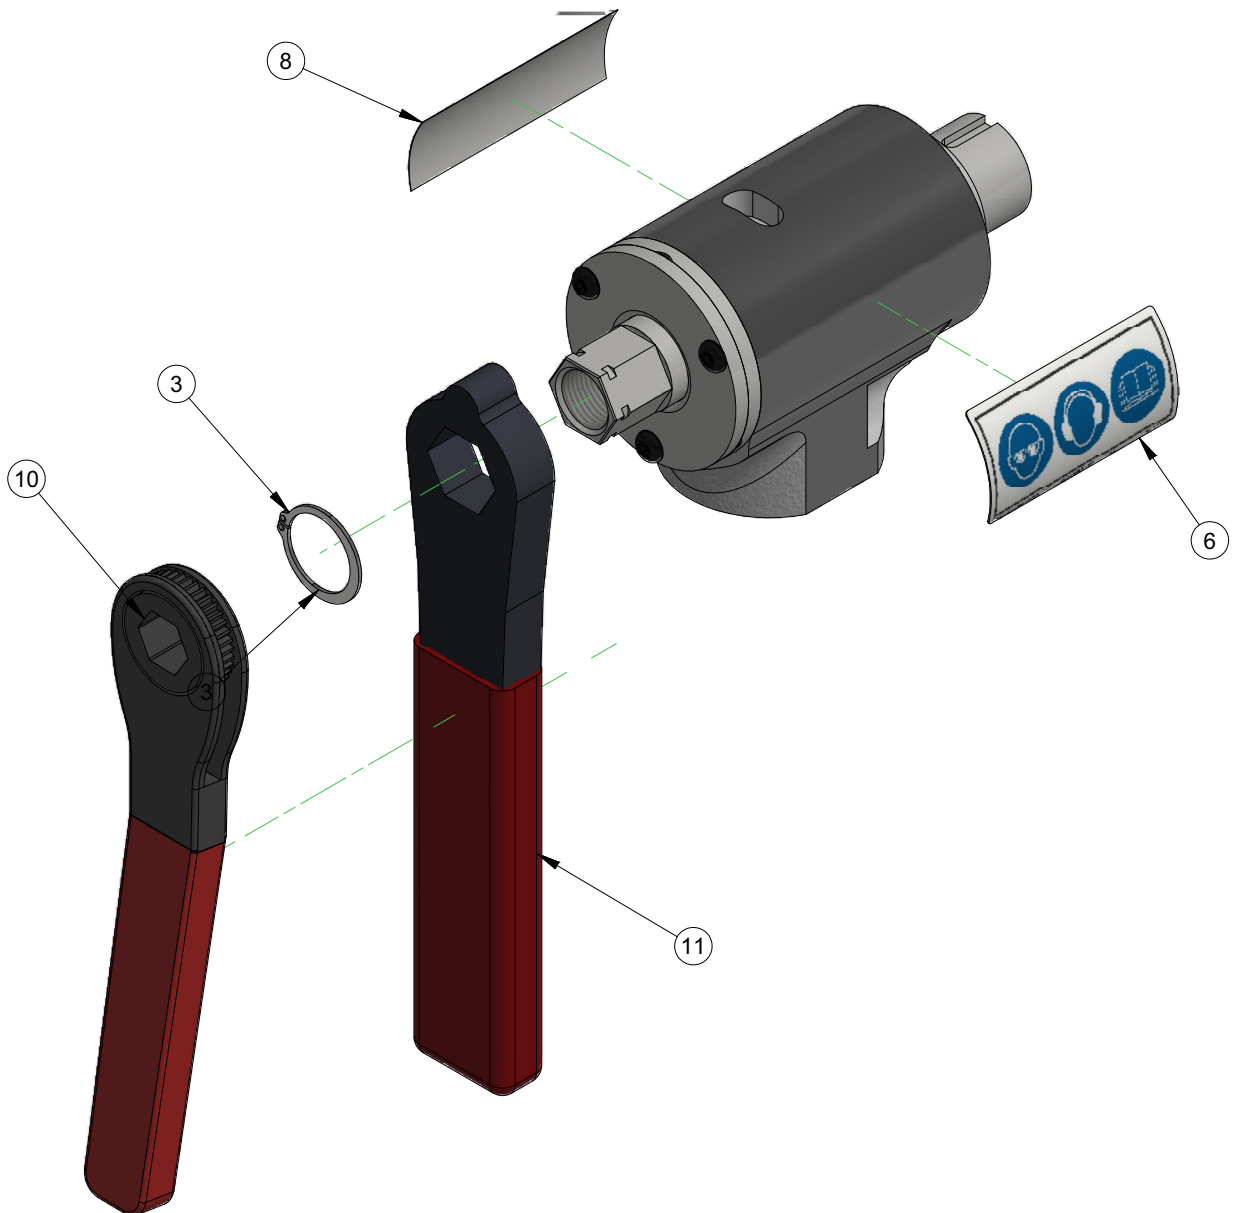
MONTAJE DE LA UNIDAD BASE 1 DE LA BF-R BOILER GUN (N/P 98894)
